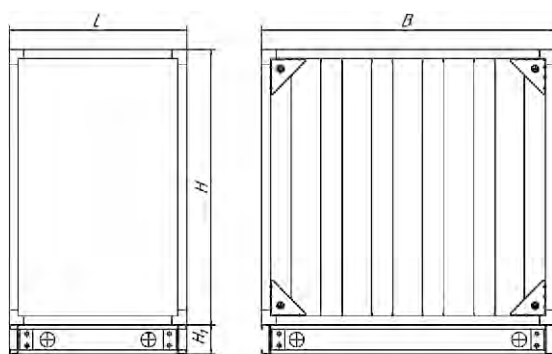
Габаритные размеры. Блок шумоглушителя.
